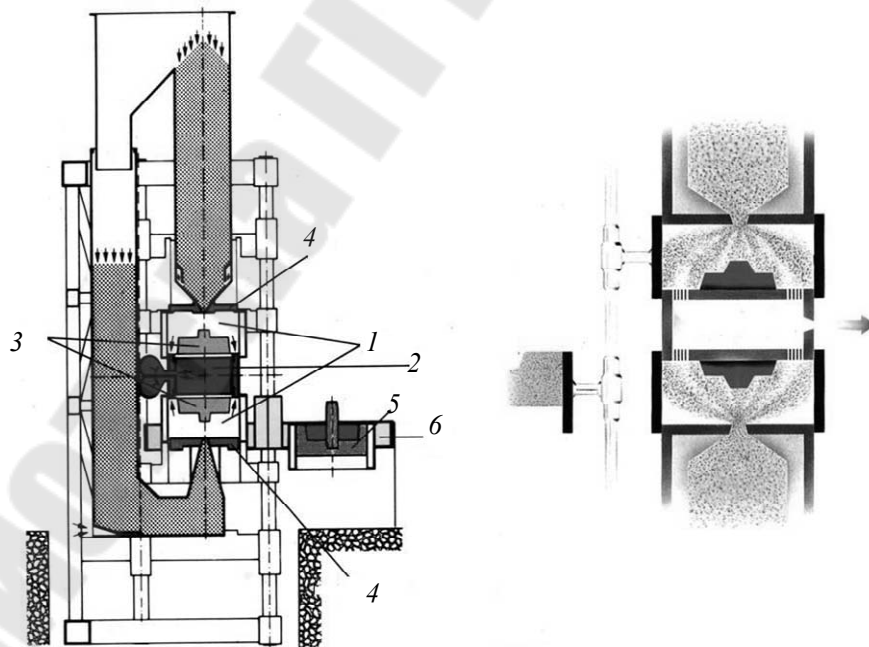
Схема базового формовочного агрегата линии Formatic: 1 – формовочная камера; 2 – камера вакуумирования; 3 – модели; 4 – пескодувно-прессовая плита; 5 – полуформа низа на позиции протановки стержней; 6 – поворотный двухпозиционный стол
